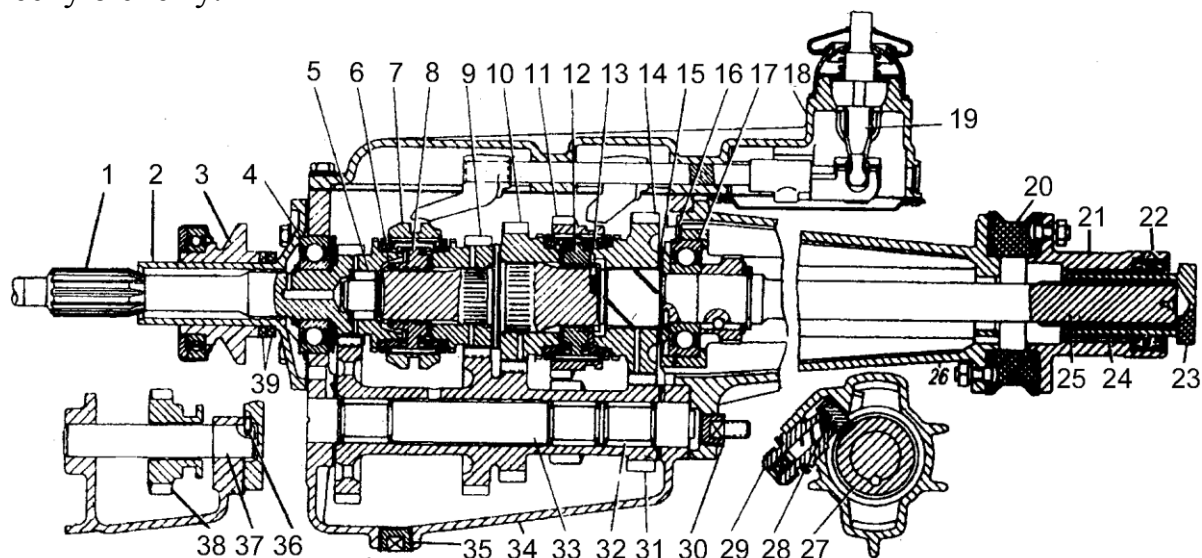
Устройство 4-х ступенчатой КПП автомобиля ГАЗ-24
